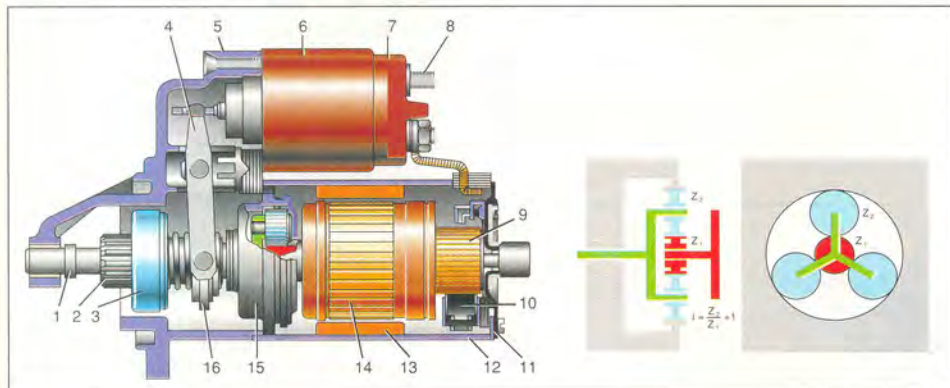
Стартер “Бош” с планетарным редуктором: 1 – ограничительное кольцо; 2 – шестерня привода; 3 – обгонная муфта; 4 – рычаг привода; 5 – крышка; 6 – тяговое реле; 7 – крышка реле; 8 – контактные болты; 9 – коллектор; 10 – щетка; 11 – крышка; 12 – корпус; 13 – постоянные магниты; 14 – якорь; 15 – планетарный редуктор; 16 – поводковое кольцо;  $i$  – передаточное число редуктора.
